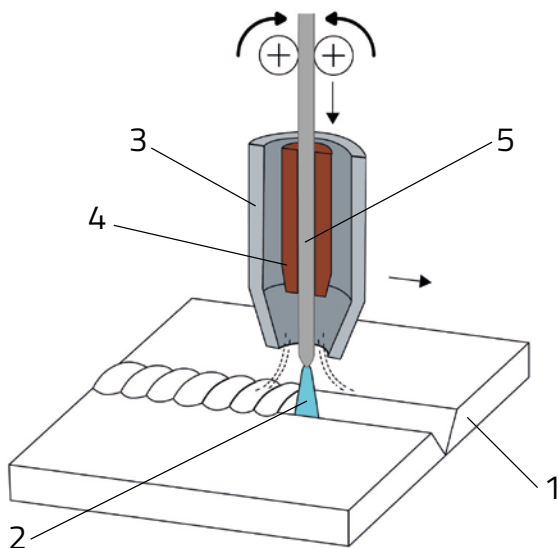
Prinzip des Metall-Schutzgasschweißens (MIG/MAG)
